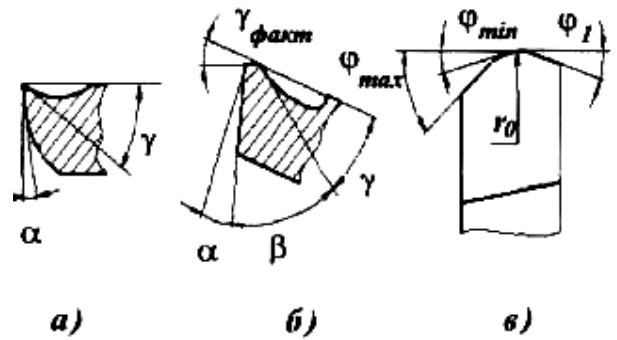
Різці із криволінійними поверхнями (а), з фаскою (б) і округленими ріжучою кромкою і вершиною (в)
